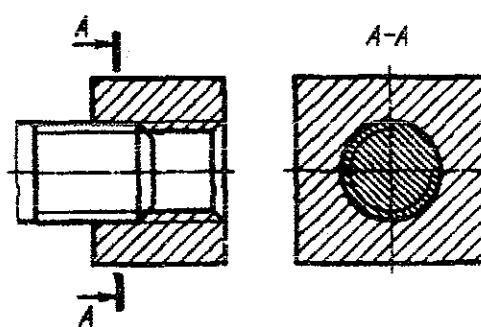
Пример изображения резьбы в резьбовых соединениях
